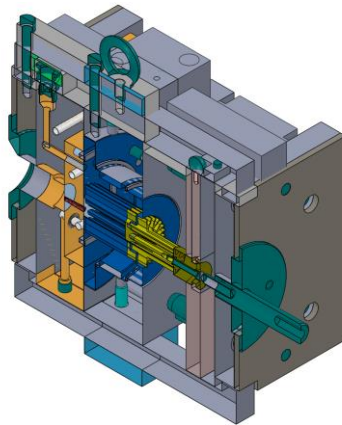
Schnittbild des Spritzgießwerkzeugs mit Formein-
